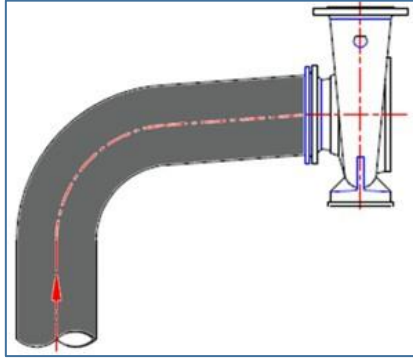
Santrifüj Pompaj Tesisi ve Elemanları
